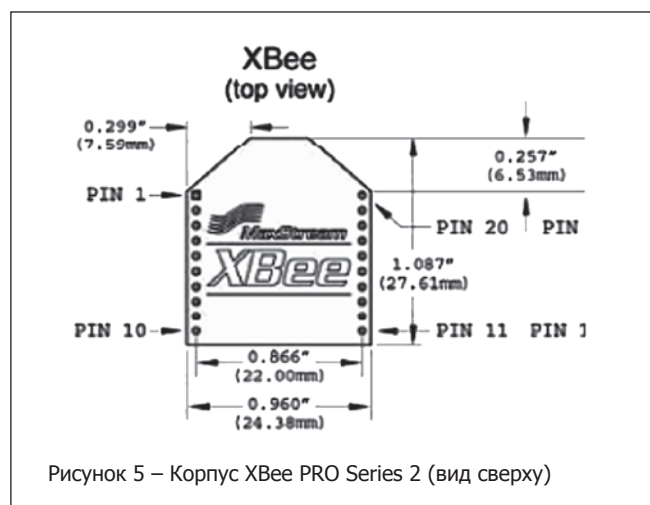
Корпус XBee PRO Series 2 (вид сверху)
